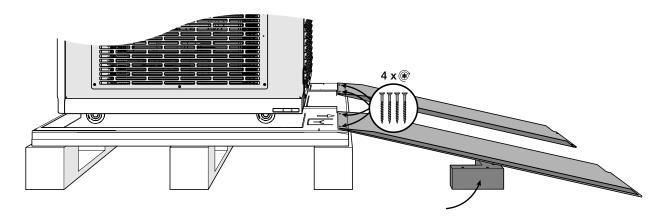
Fijación y soporte de las rampas para bajar la centrífuga
